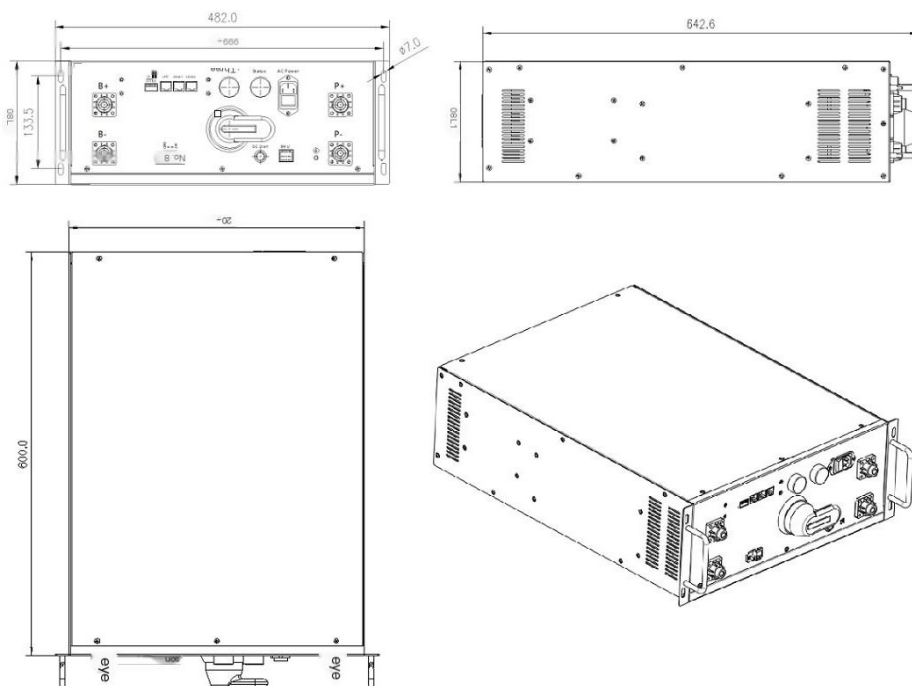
Внешний вид и установочные размеры CBMS с двумя линиями питания
